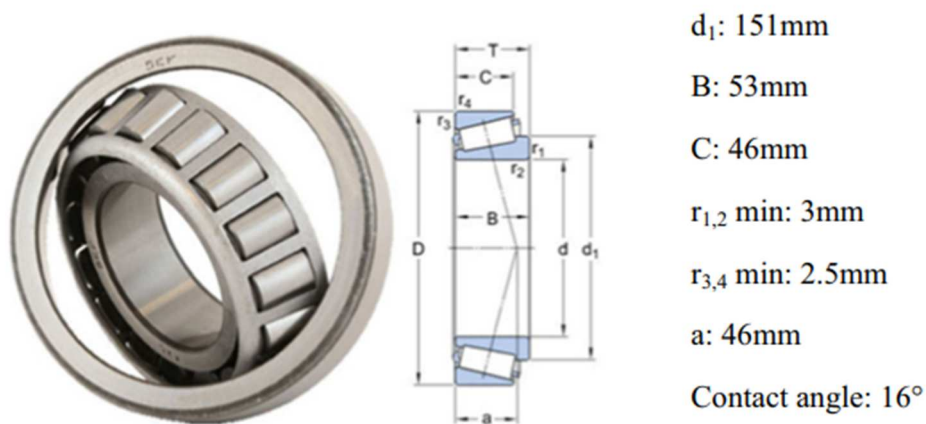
Dimensions du roulement à rouleaux coniques (SKF 32222 J2)
